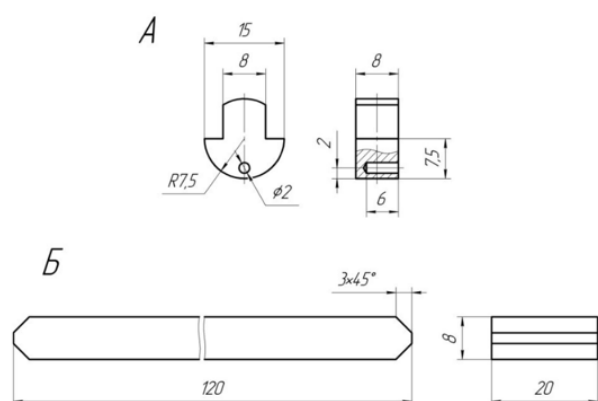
Схемы образцов: А – подвижный образец, Б – неподвижный образец
